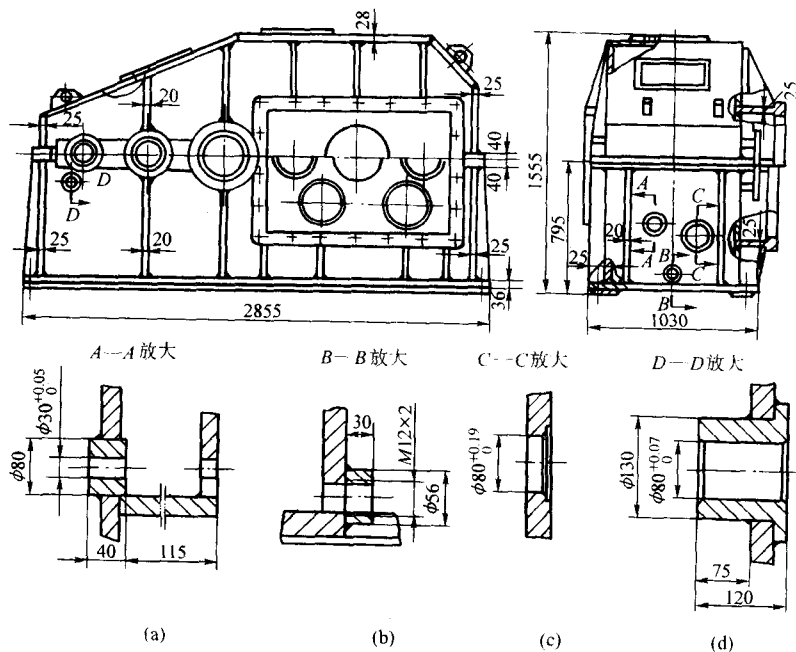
三辊弯板机减速器焊接箱体
